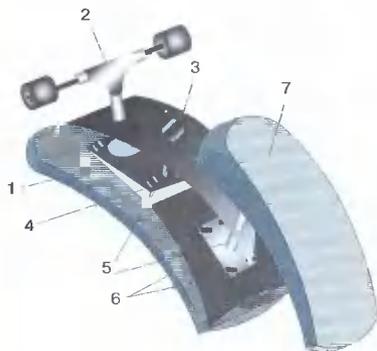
Механизм подвесок: 1 — верхняя дека; 2 — колесный трак; 3 — рычажная пластина; 4 — клинообразная подошва; 5 — стойки; 6 — кант; 7 — нижняя дека.
